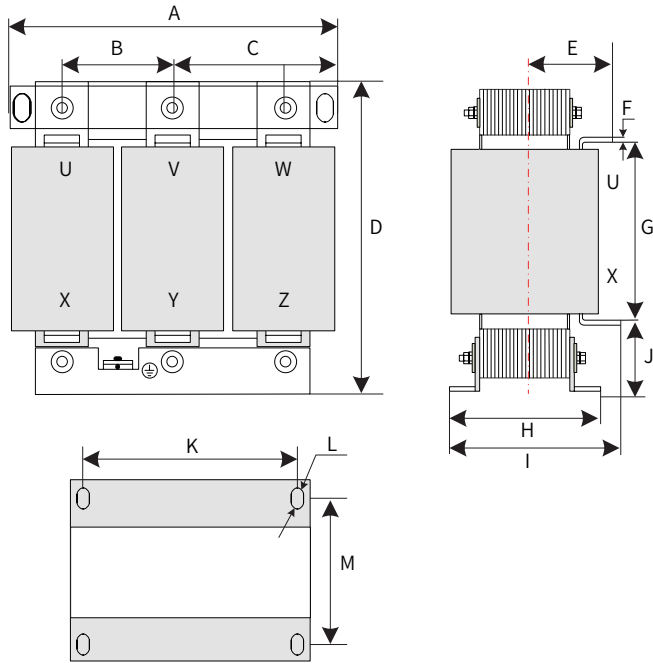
Размеры выходного реактора переменного тока 330 А
